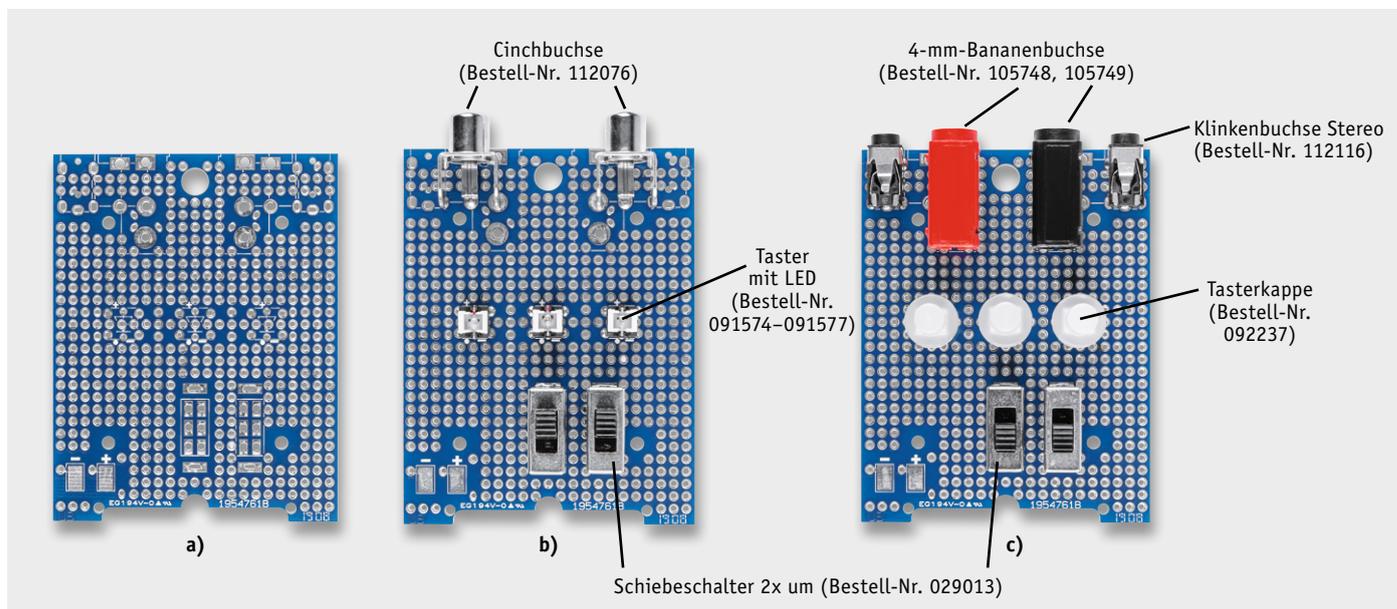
Die Platinenversion UniBox1-PCB1 mit unterschiedlicher Bestückung
